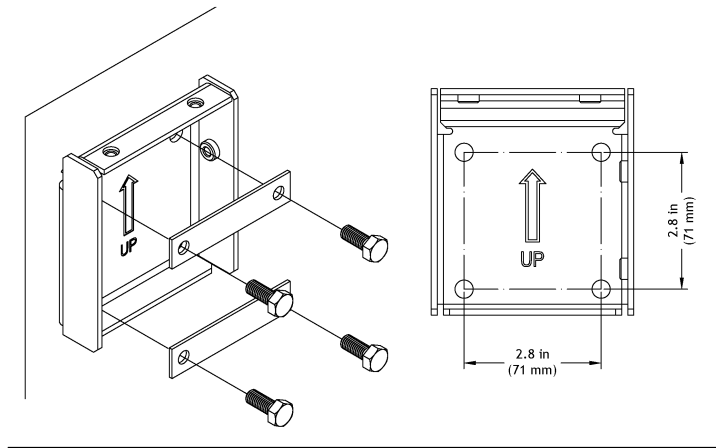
Montage der Instrumentenhalterung4.2.2 Wand- und RackmontageProzedur
